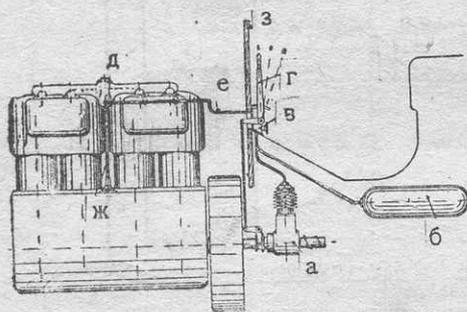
Схема автоматического пускового приспособления «Заурер»
